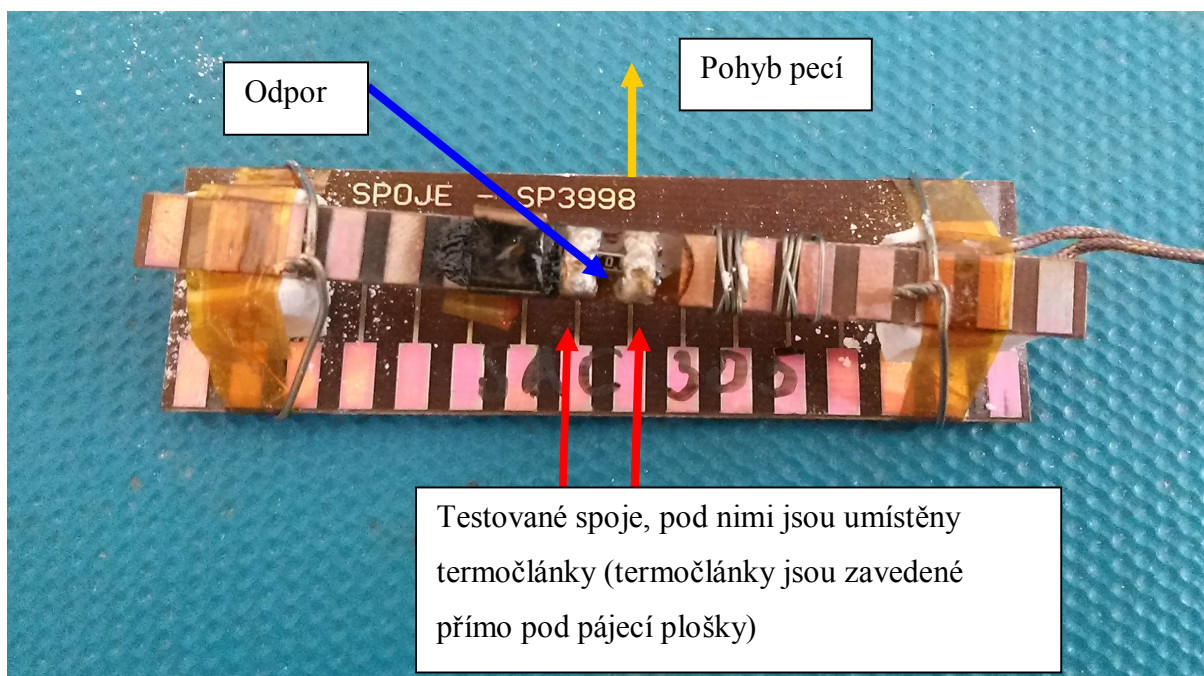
schematicky zobrazuje testovací destičku.
